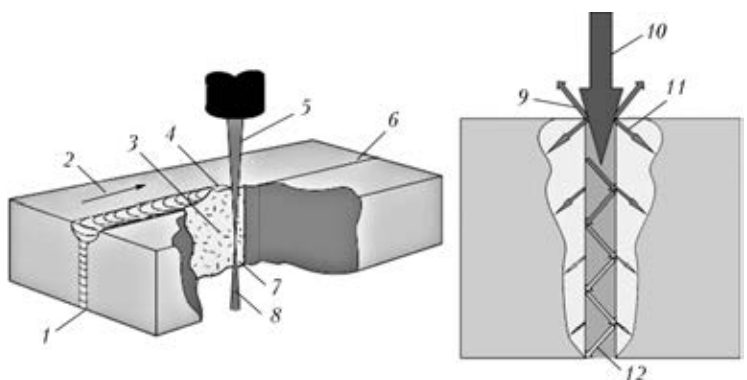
Схема процесса лазерной сварки с парогазовым каналом [4]: 1 — валик шва; 2 — направление сварки; 3 — ЗТВ; 4 — парогазовый канал; 5 — лазерный пучок; 6 — кромка шва; 7 — жидкий металл; 8 — лазерный пучок, выходящий из обрабатываемого изделия; 9 — отраженное излучение; 10 — лазерный пучок; 11 — поглощенное излучение; 12 — переотражения от стенок парогазового канала
